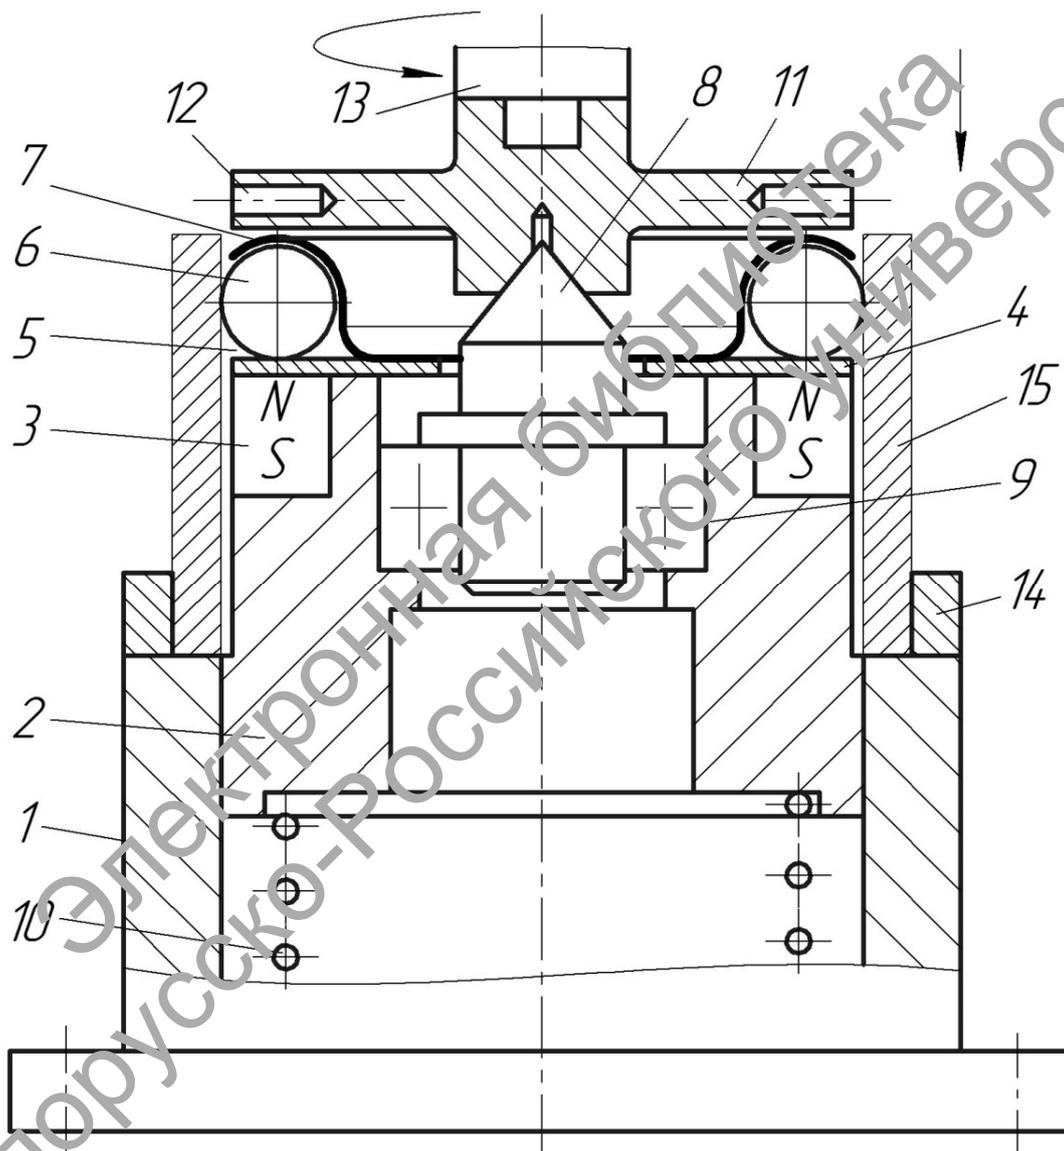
Схема инструмента с вращающимся магнитопроводом для совмещенной упрочняющей обработки внутренней поверхности цилиндров: 1 – цилиндрический корпус; 2 – шток; 3 – источник магнитного поля; 4 – шайба; 5 – кольцевая камера; 6 – деформирующие шары; 7 – кожух; 8 – вращающийся центр; 9 – подшипник; 10 – пружина; 11 – кольцевой магнитопровод; 12 – радиальные отверстия; 13 – оправка; 14 – упругое кольцо; 15 – упрочняемый цилиндр
